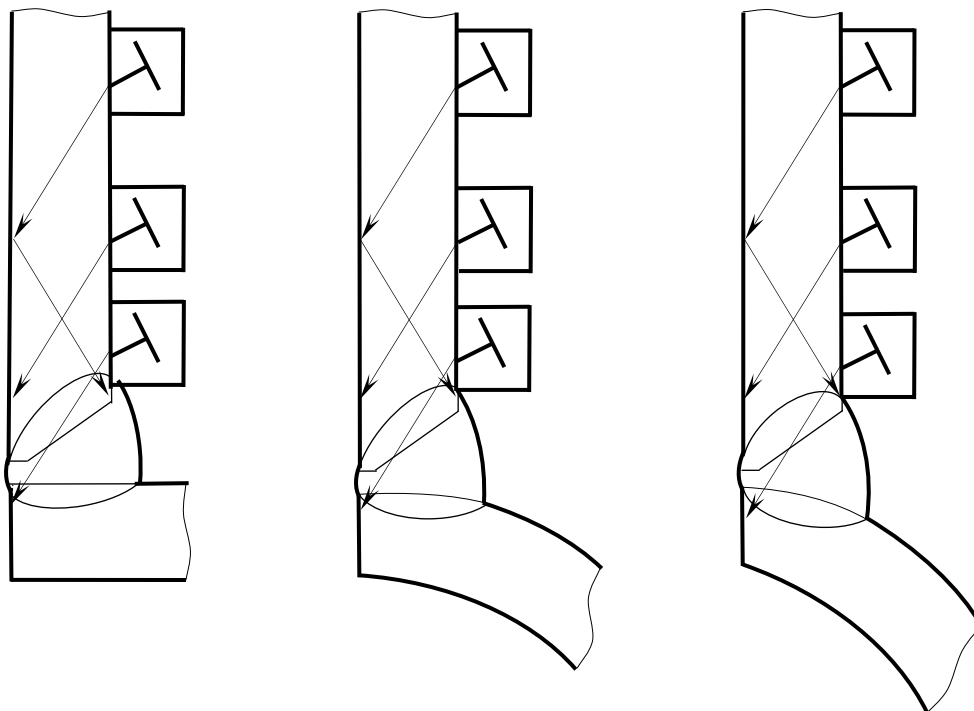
Схема контроля углового сварного соединения тройника прямыми и однократно-отраженным лучами со стороны патрубка
